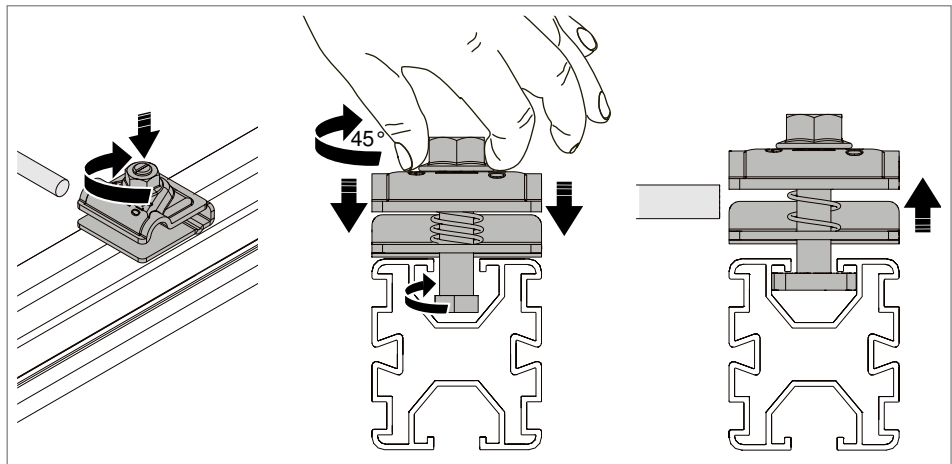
Hammerkopfschraube in Trägerprofil verkanten
